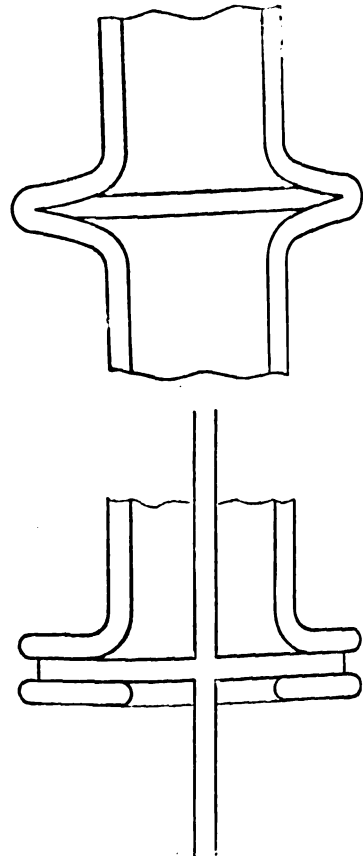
et 5. — Soudures d'un disque de laiton au verre : 1° avec enrobage des bords; 2° les bords étant libres.
